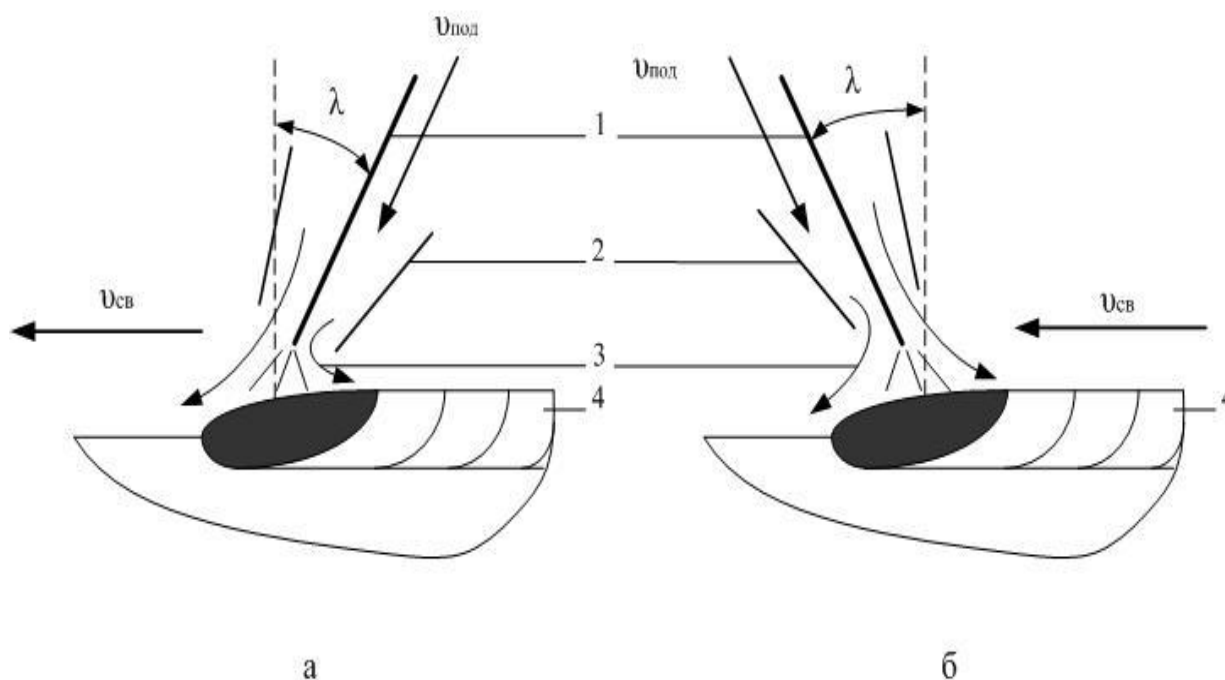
Способы полуавтоматической сварки в углекислом газе: а) углом вперед; б) углом назад; 1-проволока; 2-сопло; 3-защитный газ; 4-сварной шов.
